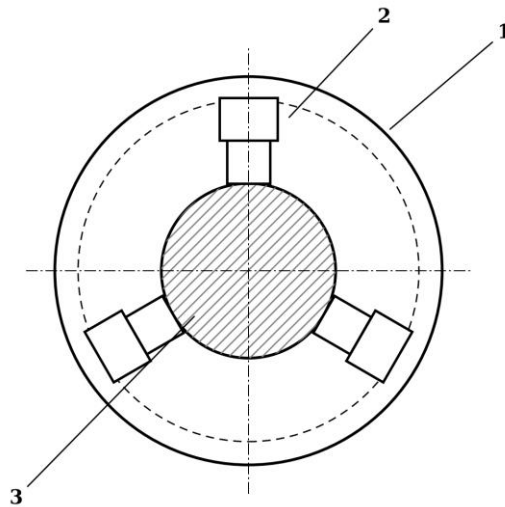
Схема трикулачкового самоцентрувального патрона: 1 – корпус;
